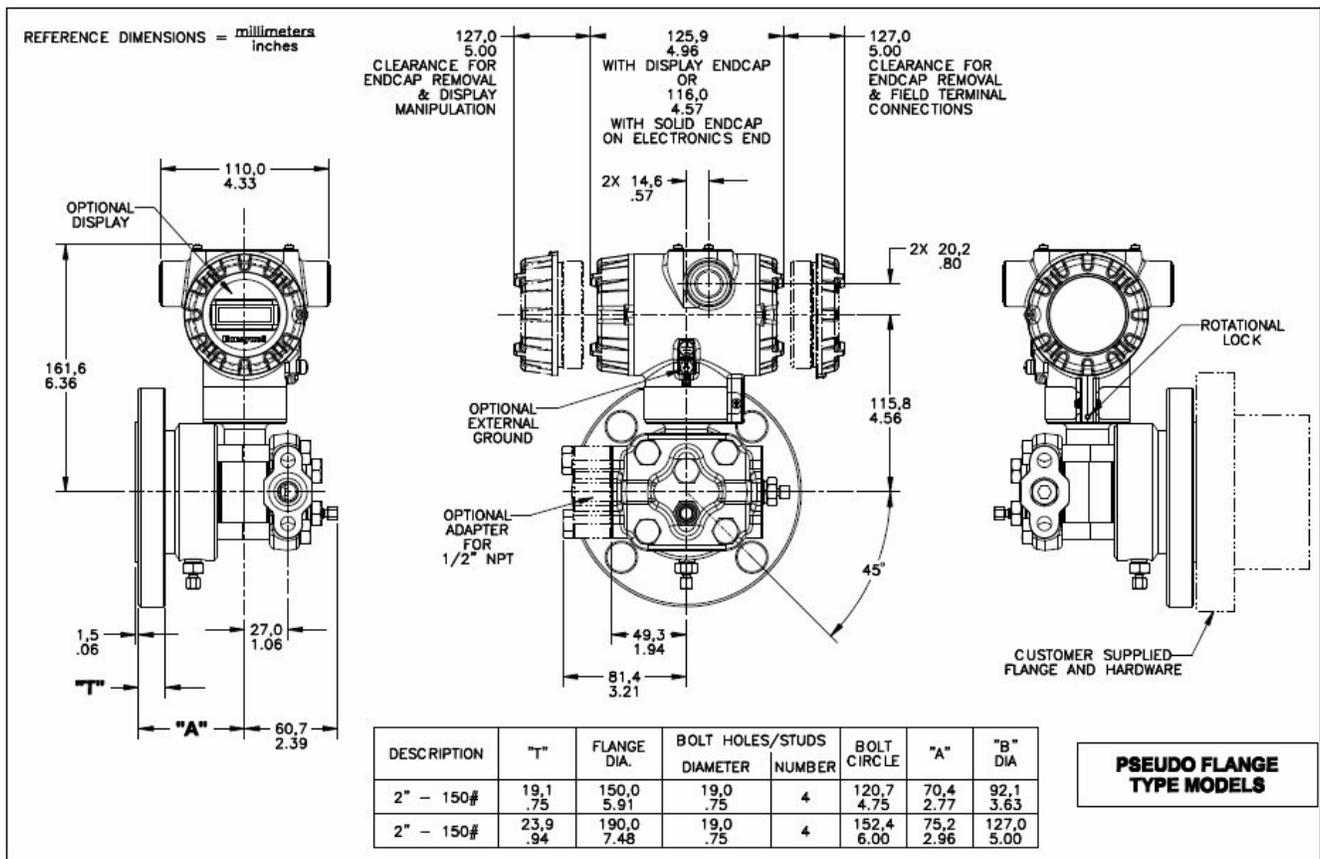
Dimensiuni de Montaj pentru Modelele cu pseudo flanse STF82F, STF83F, si STF84F.
